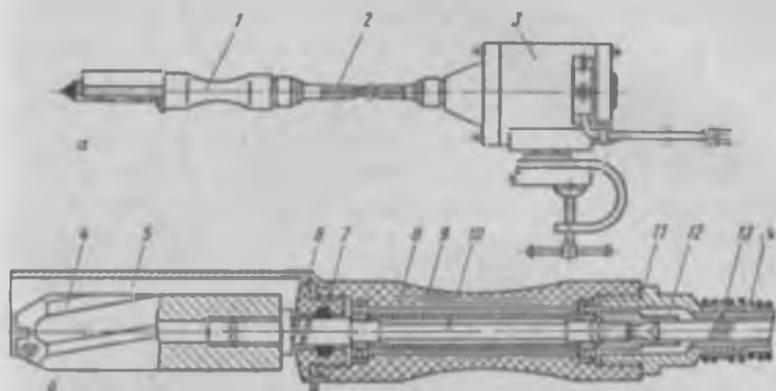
, Приспособление для очистки рыбы РО-1М:
